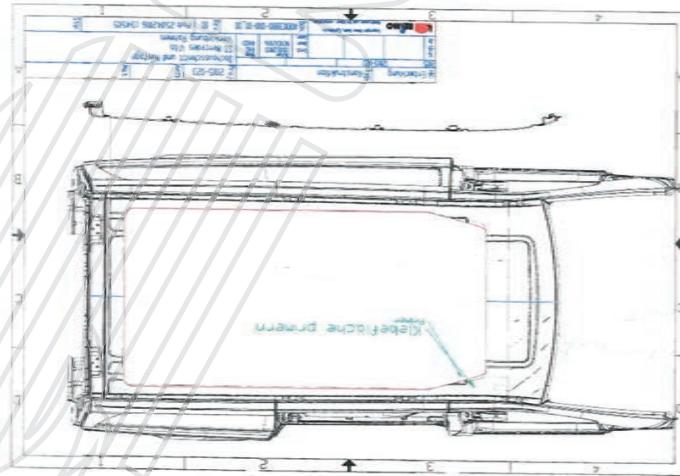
Zeichnung Dachausschnitt 1
